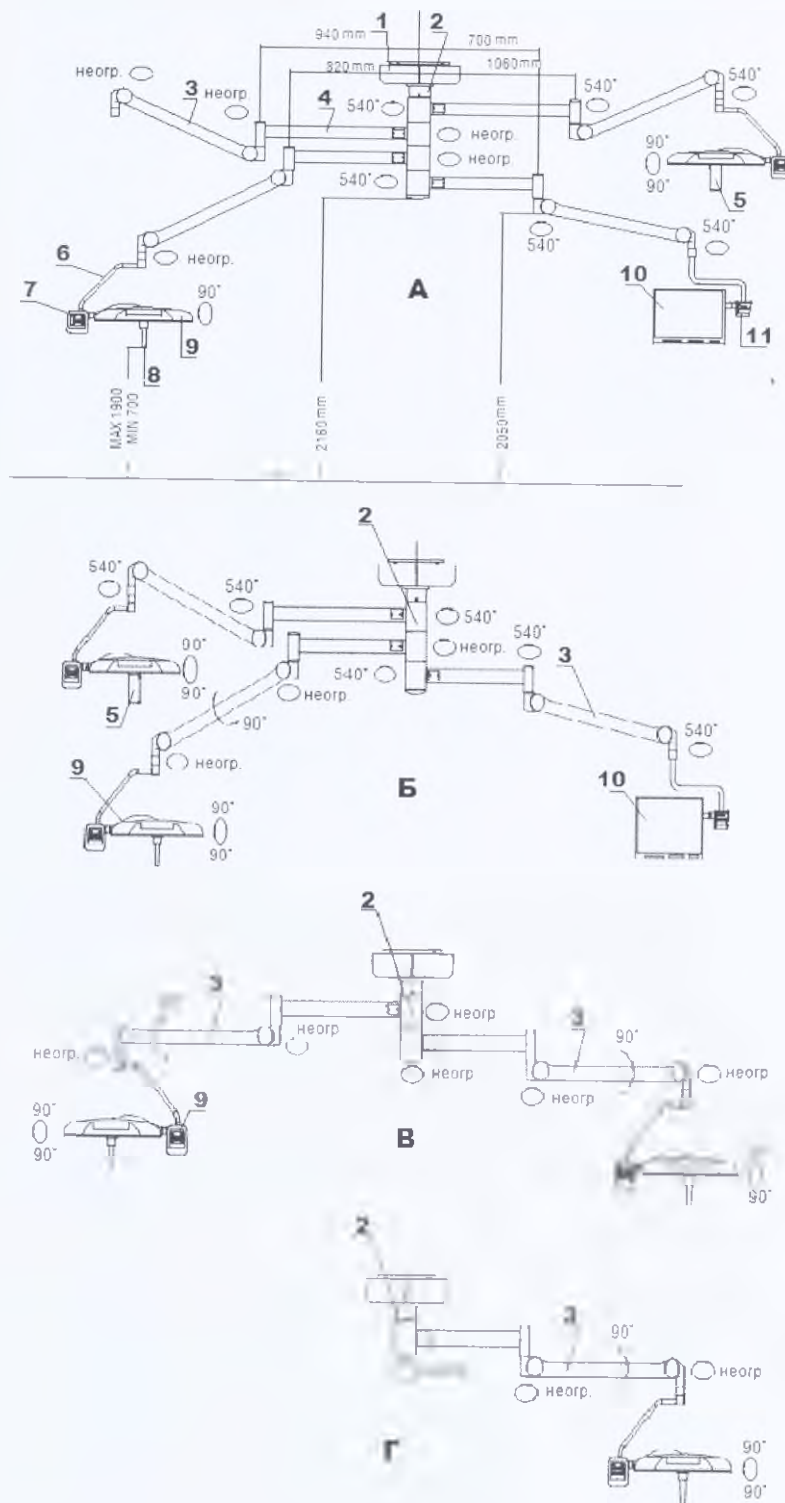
Основные размеры и углы поворота подвижных частей в шарнирах для исполнений светильников с потолочным креплением.
